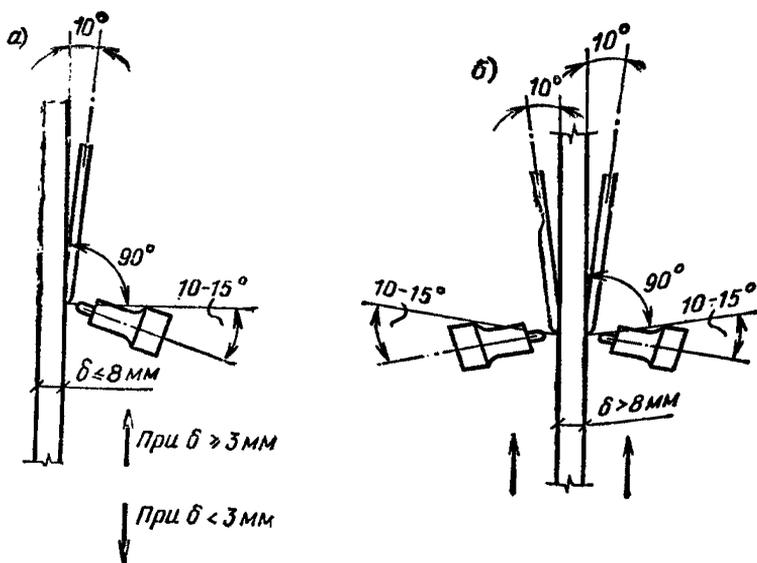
Расположение горелки и присадочного прутка при сварке в вертикальном положении
